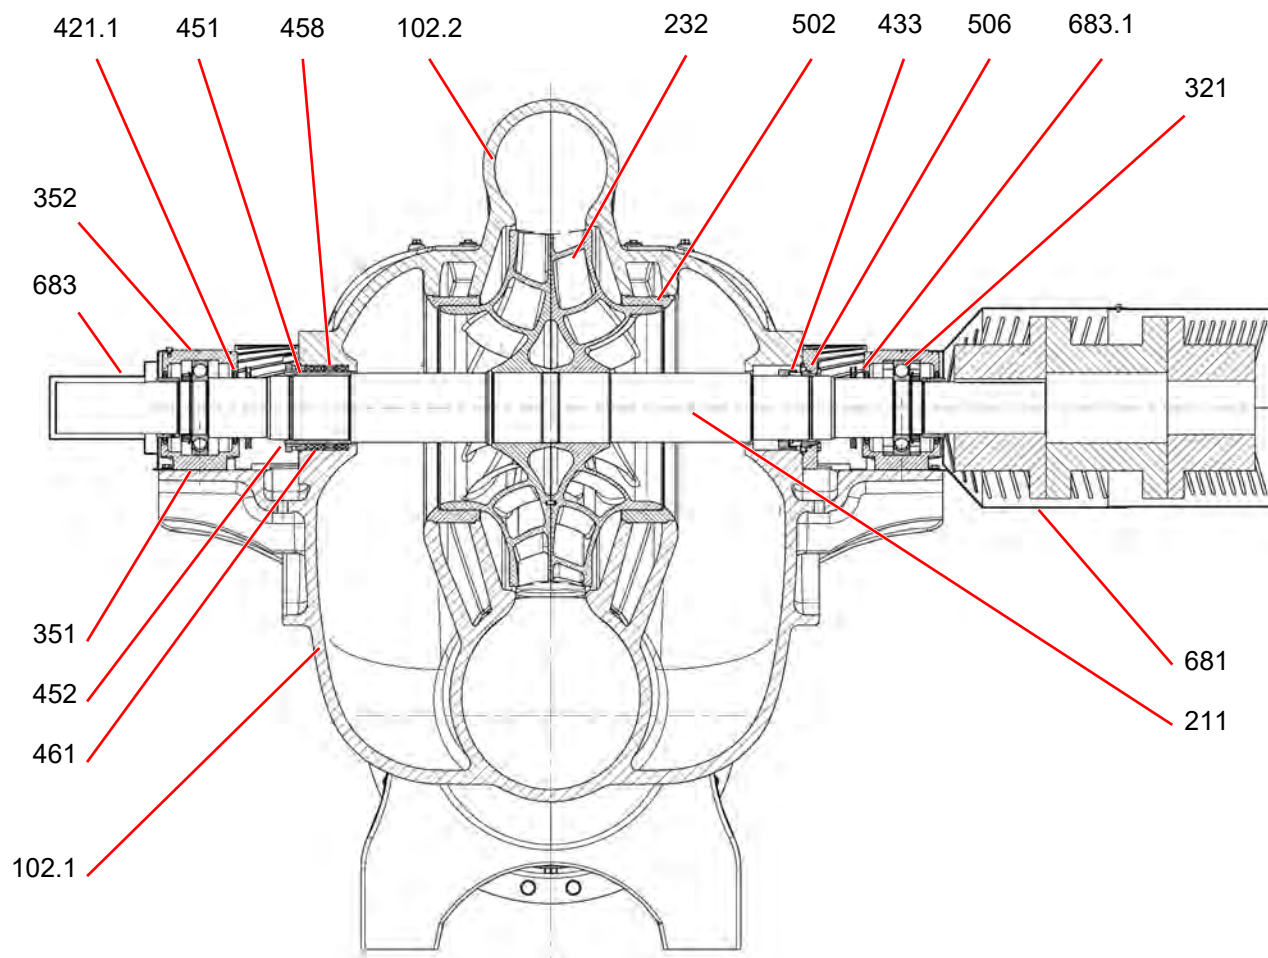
Чертеж насоса ASP-A.S в разрезе (смещенные лопасти рабочего колеса, прессовая посадка)
